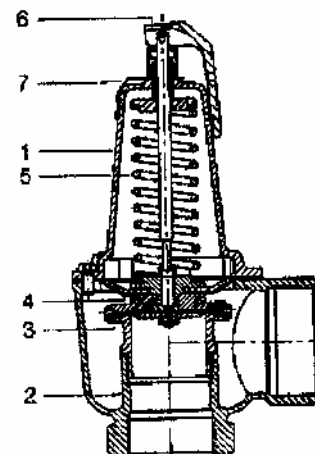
Предохранительный клапан Prescor S 1700-2
